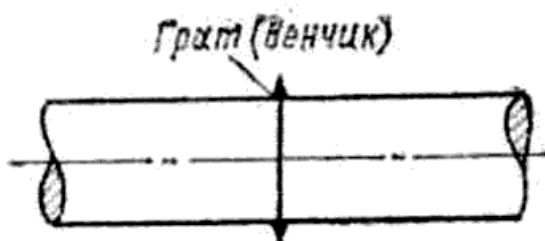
Внешний вид шва, выполненного стыковой сваркой
